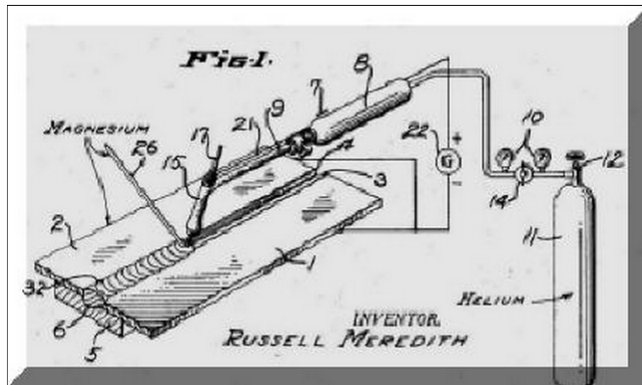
Sistema de soldagem TIG patenteado por Russel Meredith
